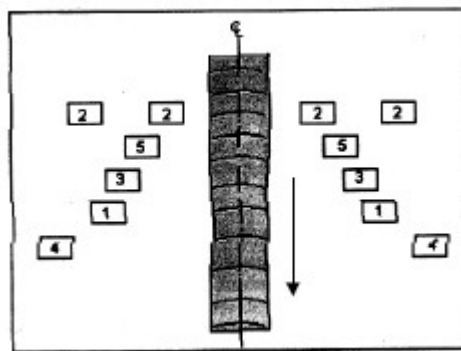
Sistema multiplexador para inspeção de juntas soldadas.
